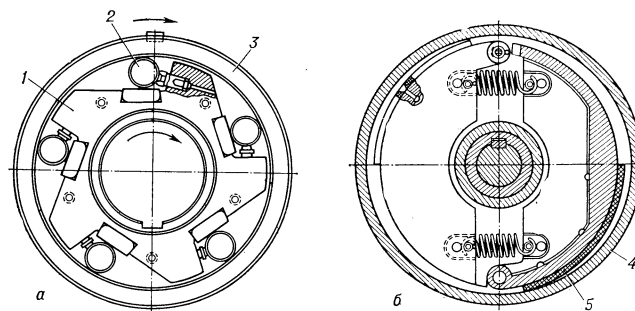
Самоуправляемые муфты: а — свободного хода; б — центробежная; в — ведущая звёздочка; г — ролики; д — ведомая обойма; е — корпус; ж — фрикционная обкладка.
